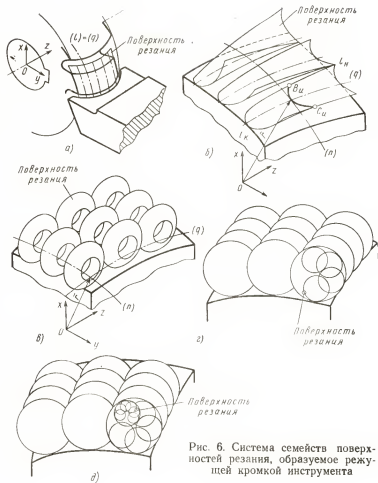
Система семейств поверхностей резания, образуемое режущей кромкой инструмента
